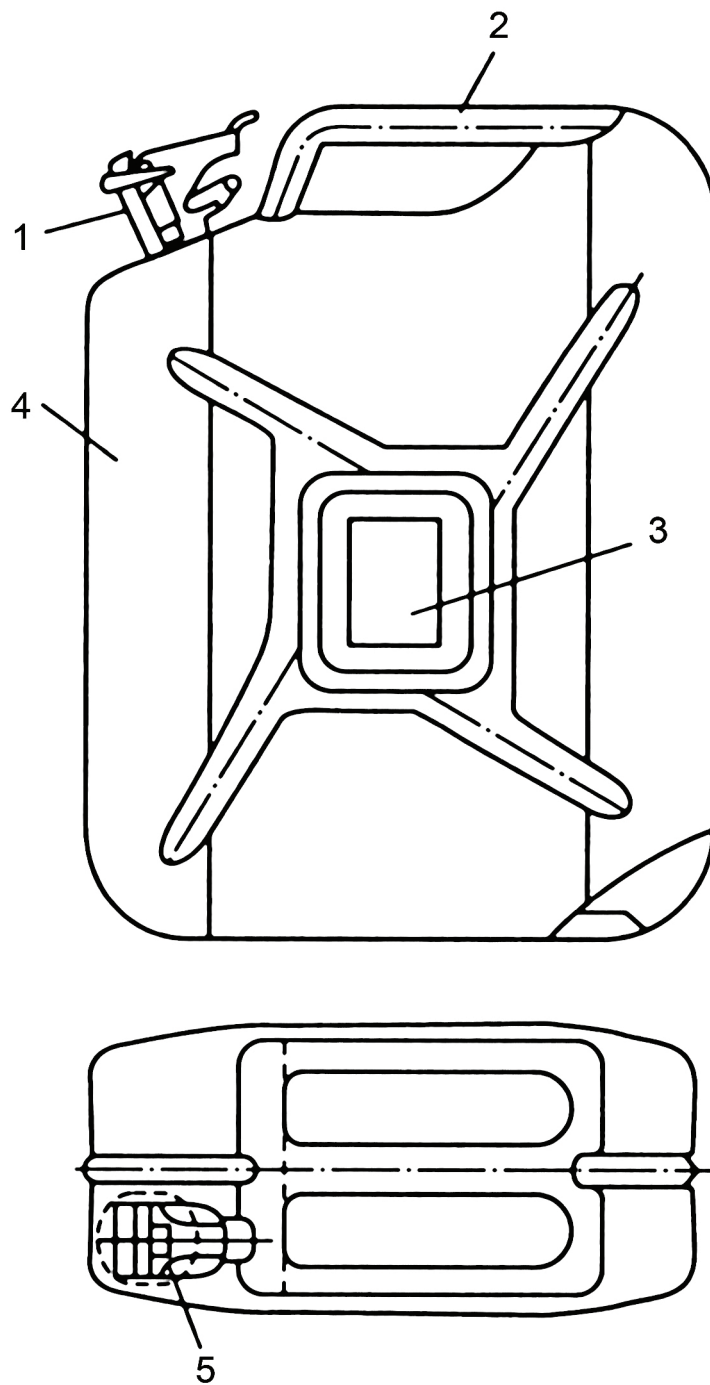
Загальний вид сталевій каністри: 1 — горловина; 2 — ручка; 3 — місце для товарного знаку; 4 — корпус; 5 — місце нанесення року виготовлення
